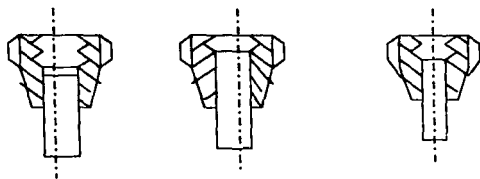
Fig. V.b. De izquierda a derecha: Cono demasiado corto, corte defectuoso y abocardado correctos.
